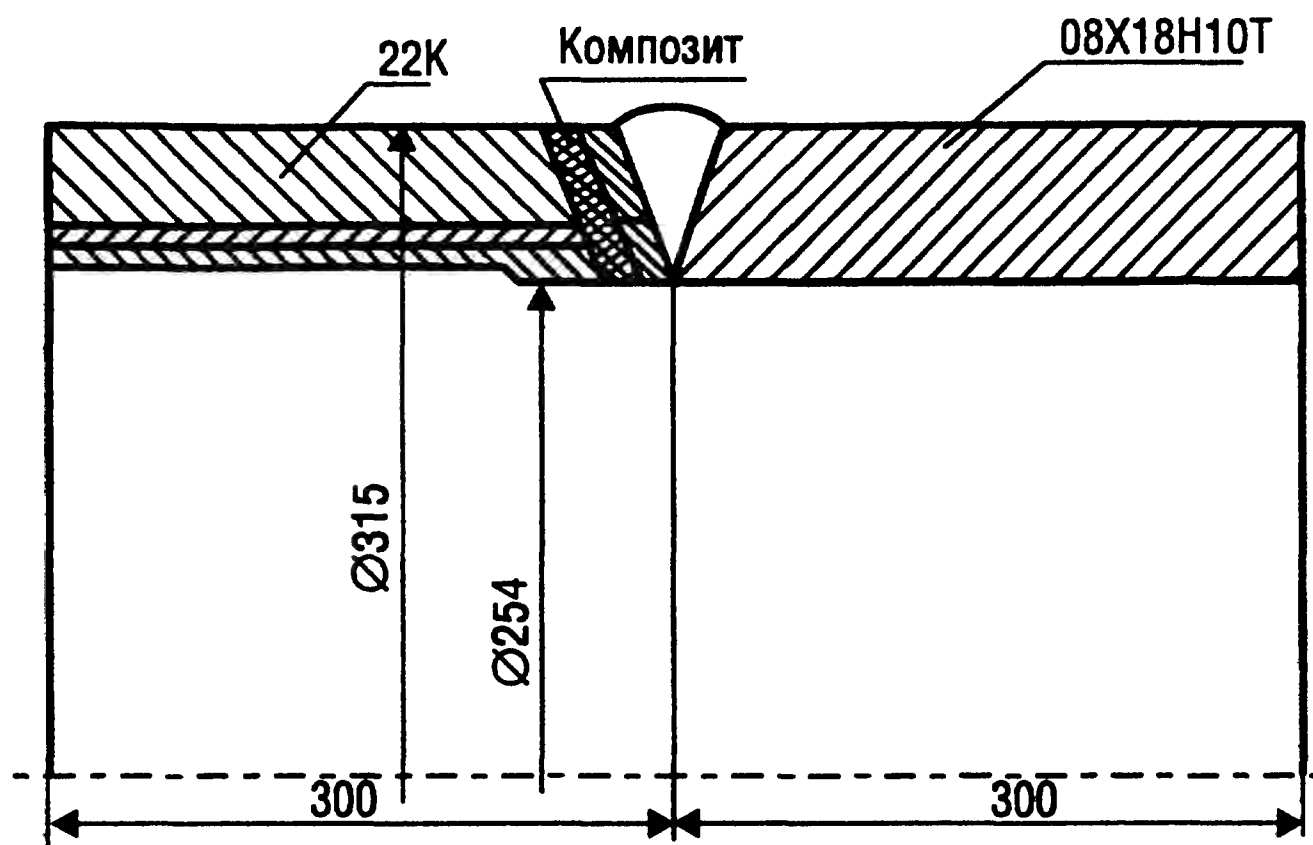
Конструкция исследуемого сварного стыка с дефектом
